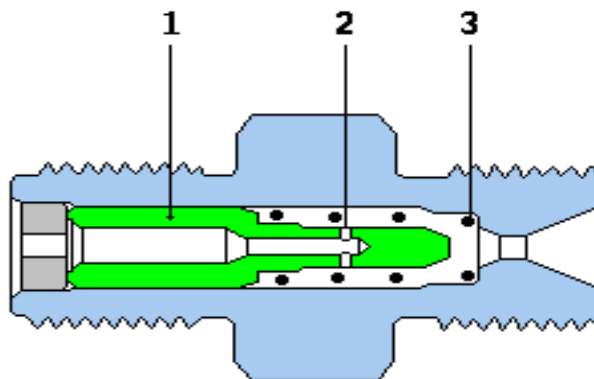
Конструкция аварийного ограничителя подачи через форсунку CR Bosch
